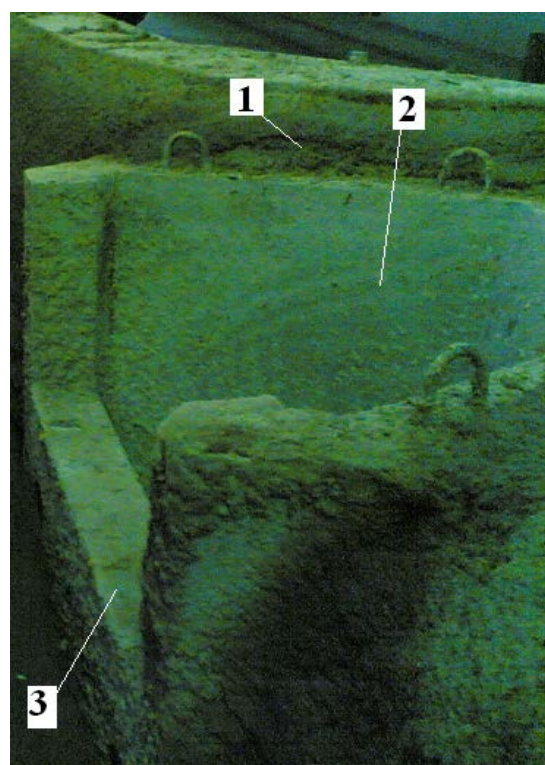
Модуль для защиты приемной камеры при подаче стали в приемную камеру промежуточного ковша: 1 – борт приемной камеры; 2 – защитное устройство; 3 – порог для защиты разливочного отверстия
